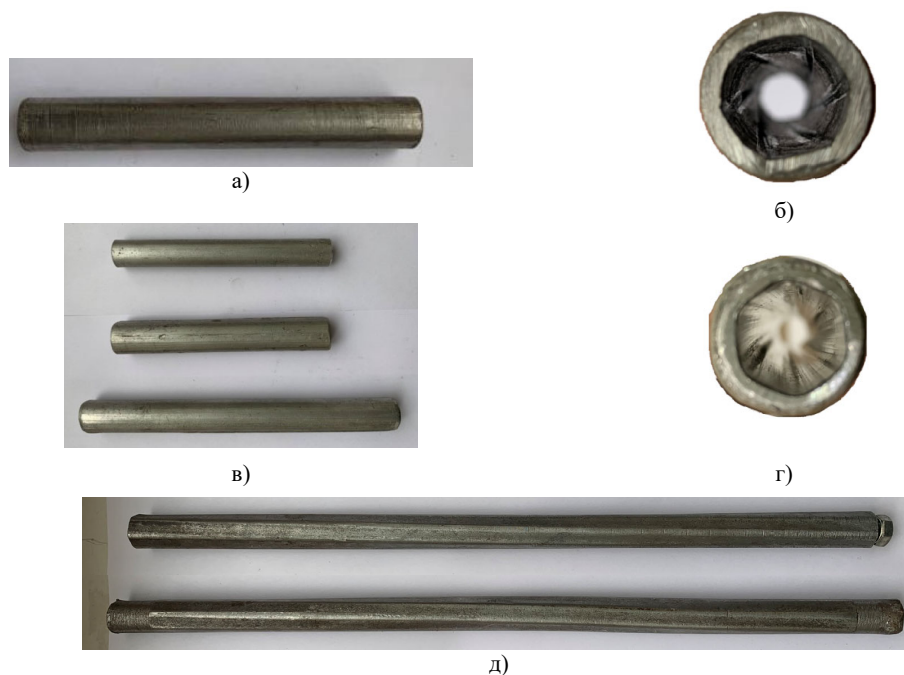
Деталі після обробки: а, в – вигляд зовнішньої циліндричної поверхні, Сталь 20, алюміній Д18 відповідно; б, г – внутрішня гвинтова поверхня, поперечний вид Сталь 45, алюміній Д18 відповідно; д – гвинтова оправка з профілем внутрішнього каналу
